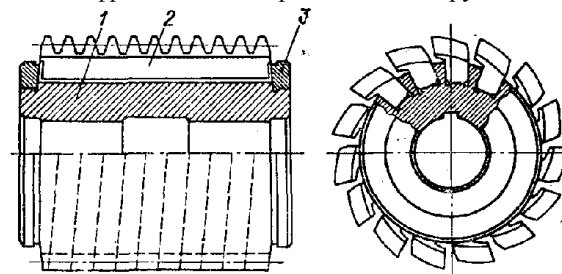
Сборная червячная фреза с поворотными рейками фирмы "Klingelberg":
